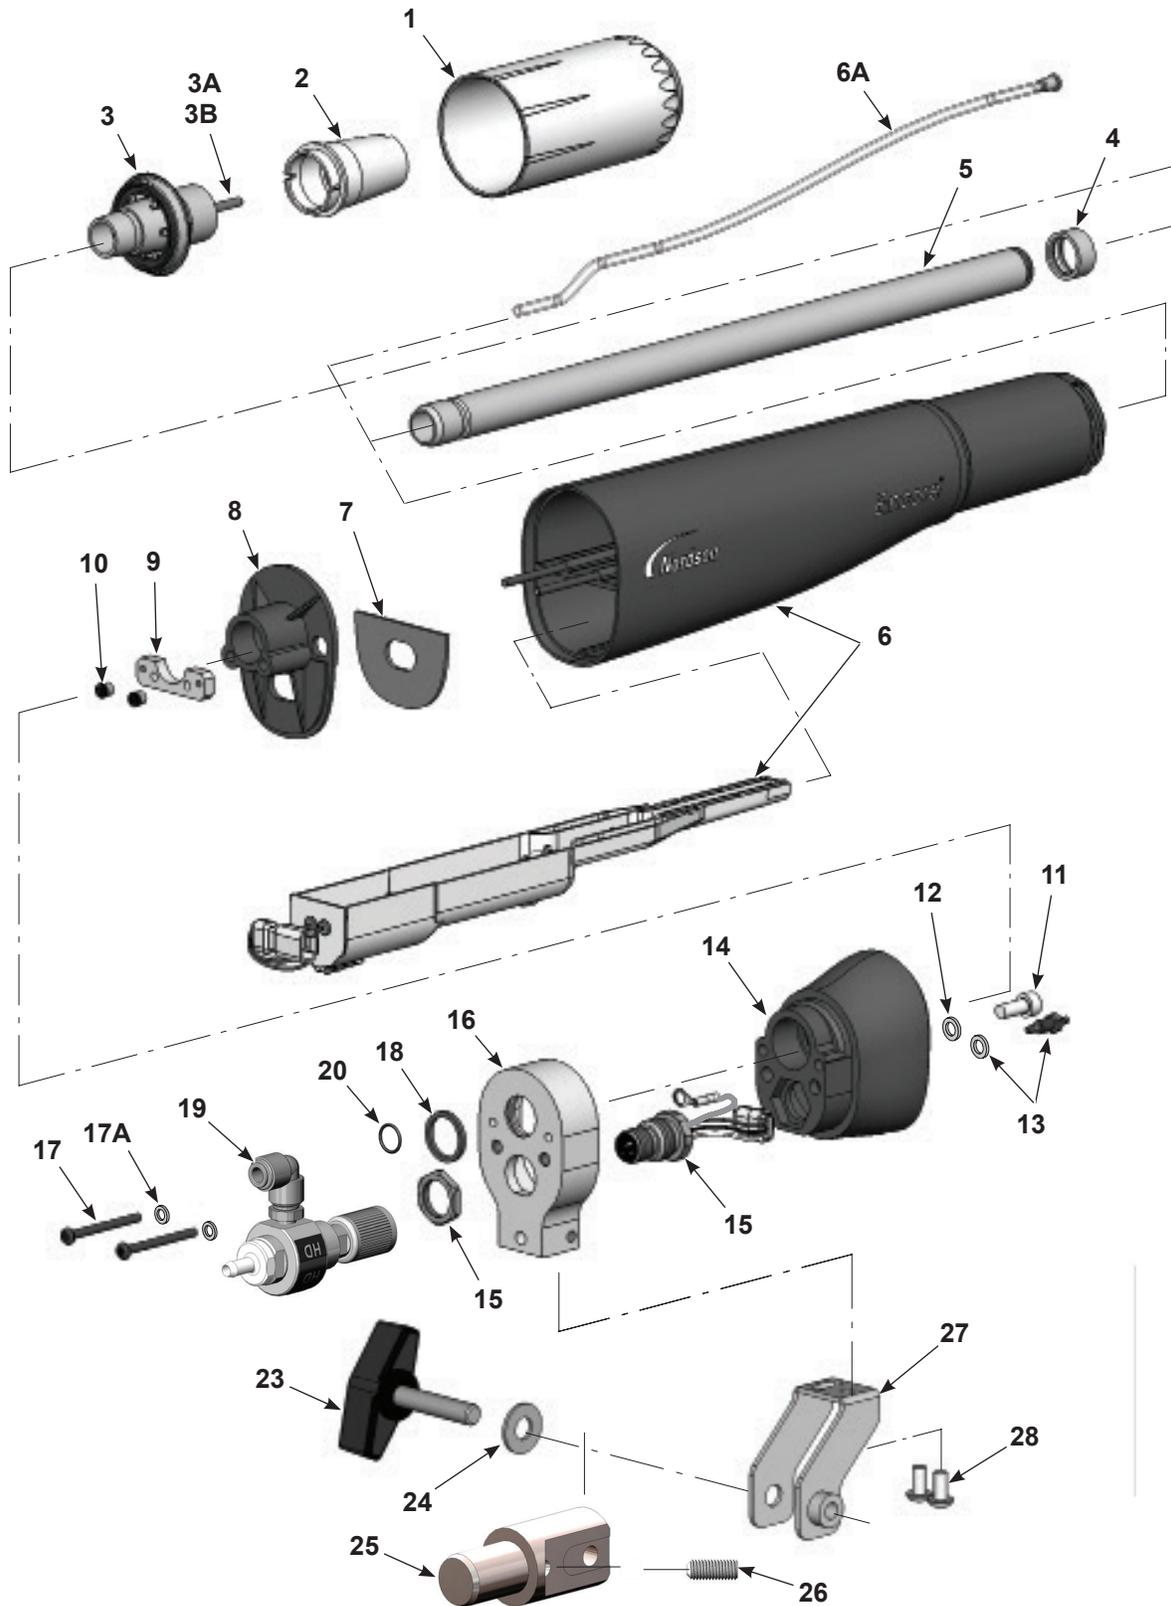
Piezas de una pistola de aplicación de montaje en barra
